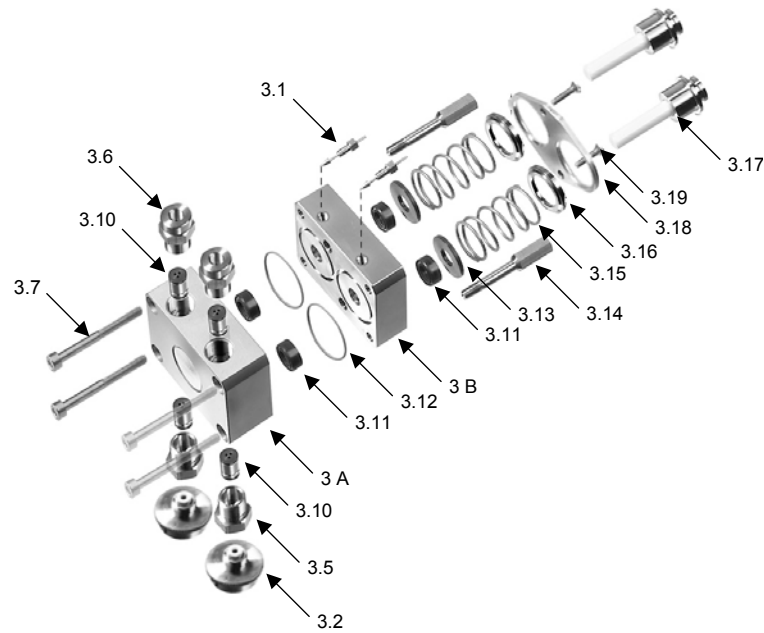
Explosionsdarstellung eines Pumpenkopfes
